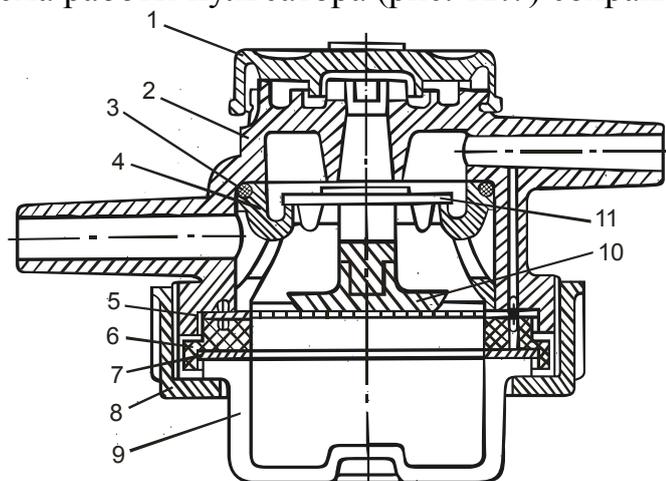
Пульсатор АДУ-1-03: расставьте правильно обозначения деталей – крышка; – корпус; – прокладка; – камера; – шайба; – клапан. – диффузор; – мембрана; – кольцо; – прокладка; – гайка;
